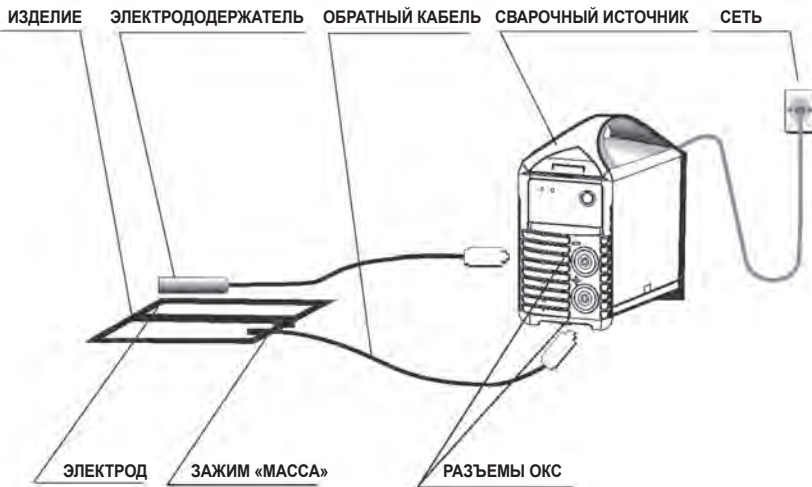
Схема подключения оборудования для ММА сварки
